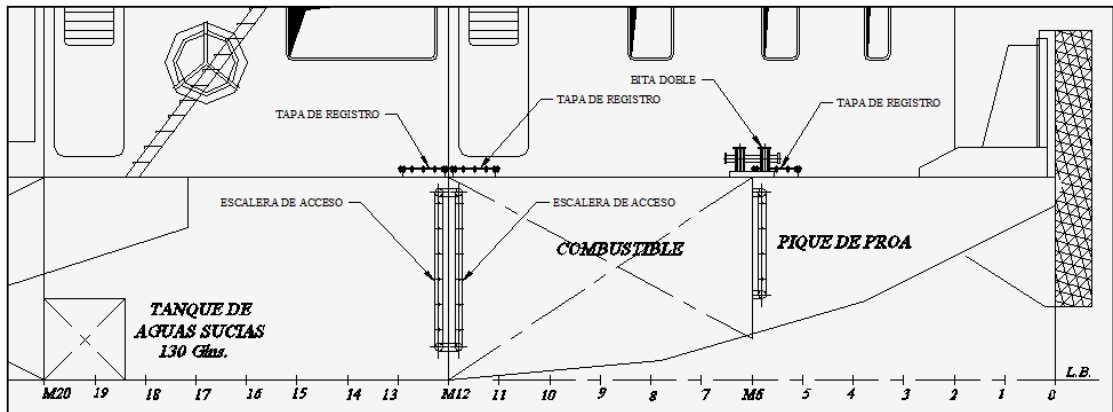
Vista longitudinal lado de estribor, ubicación de tapas de registro y escaleras de la zona de proa a partir de la sección media.
